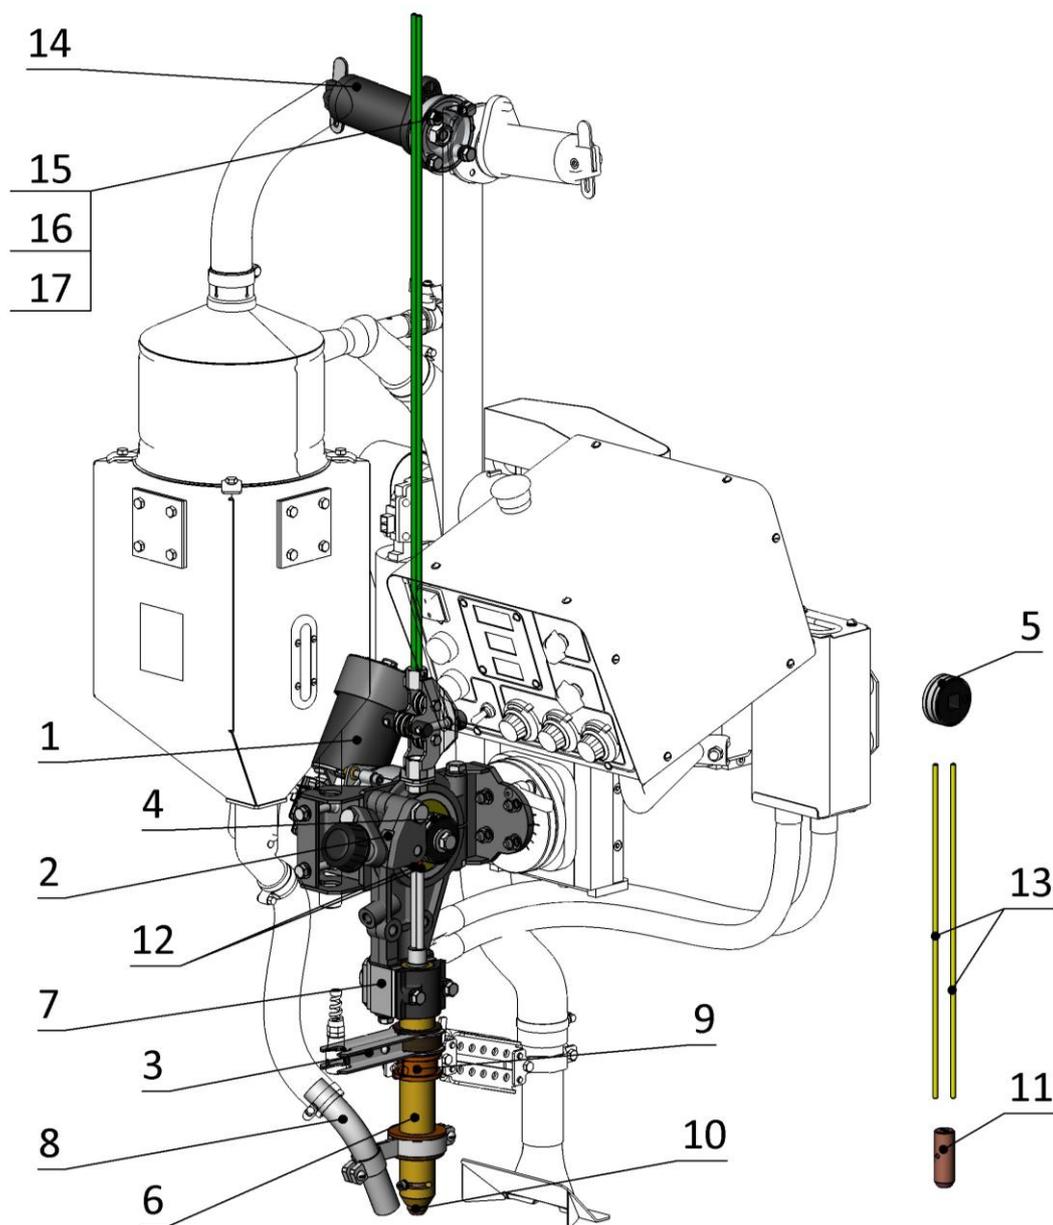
Комплект сварочной головки TWIN min для сварки двумя проволоками $\varnothing 1,2-2,0$ мм.
